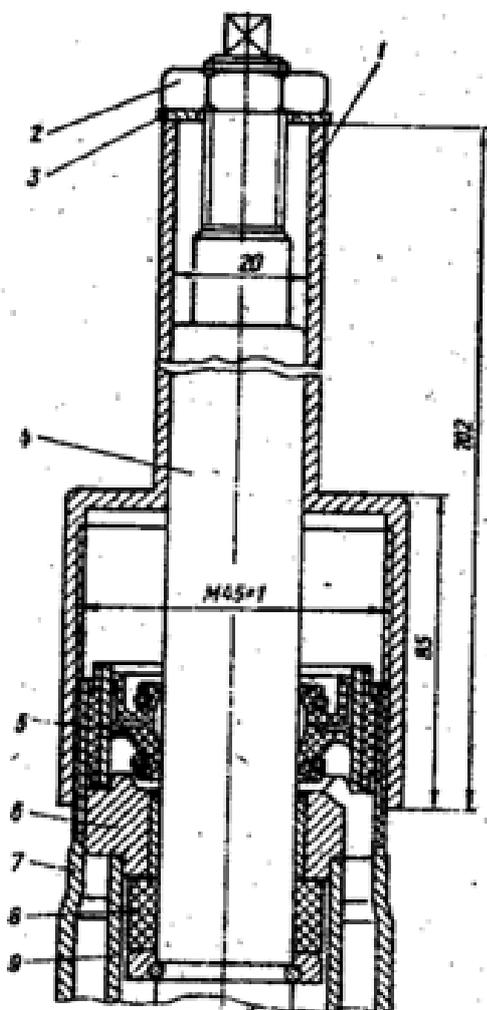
Съемник 9810-1017 для выпрессовки сальника штока амортизатора передней подвески: 1 - съемник; 2 - гайка; 3 - шайба; 4 - шток; 5 - сальник; 6 - направляющая штока; 7 - резервуар; 8 - буфер хода отдачи; 9 - цилиндр
